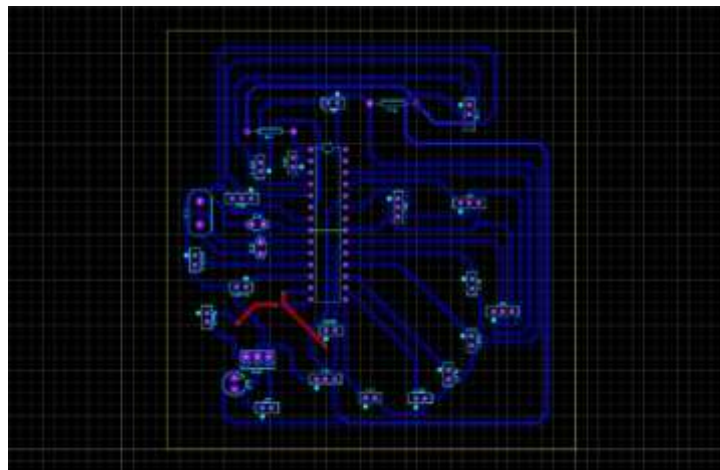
Projeto da PCB gerada pelo Proteus a partir do esquema elétrico do painel
